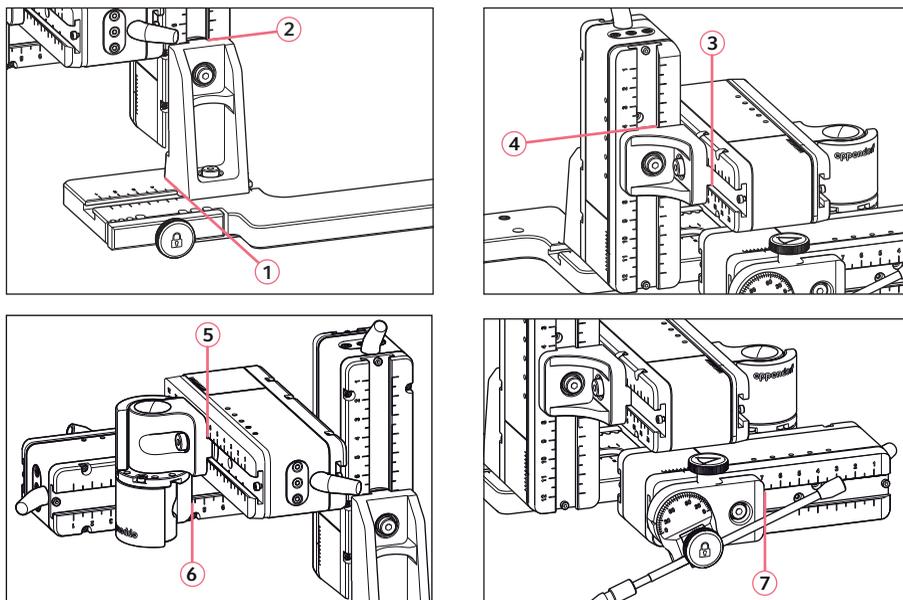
Posizioni di lettura dei parametri di montaggio
